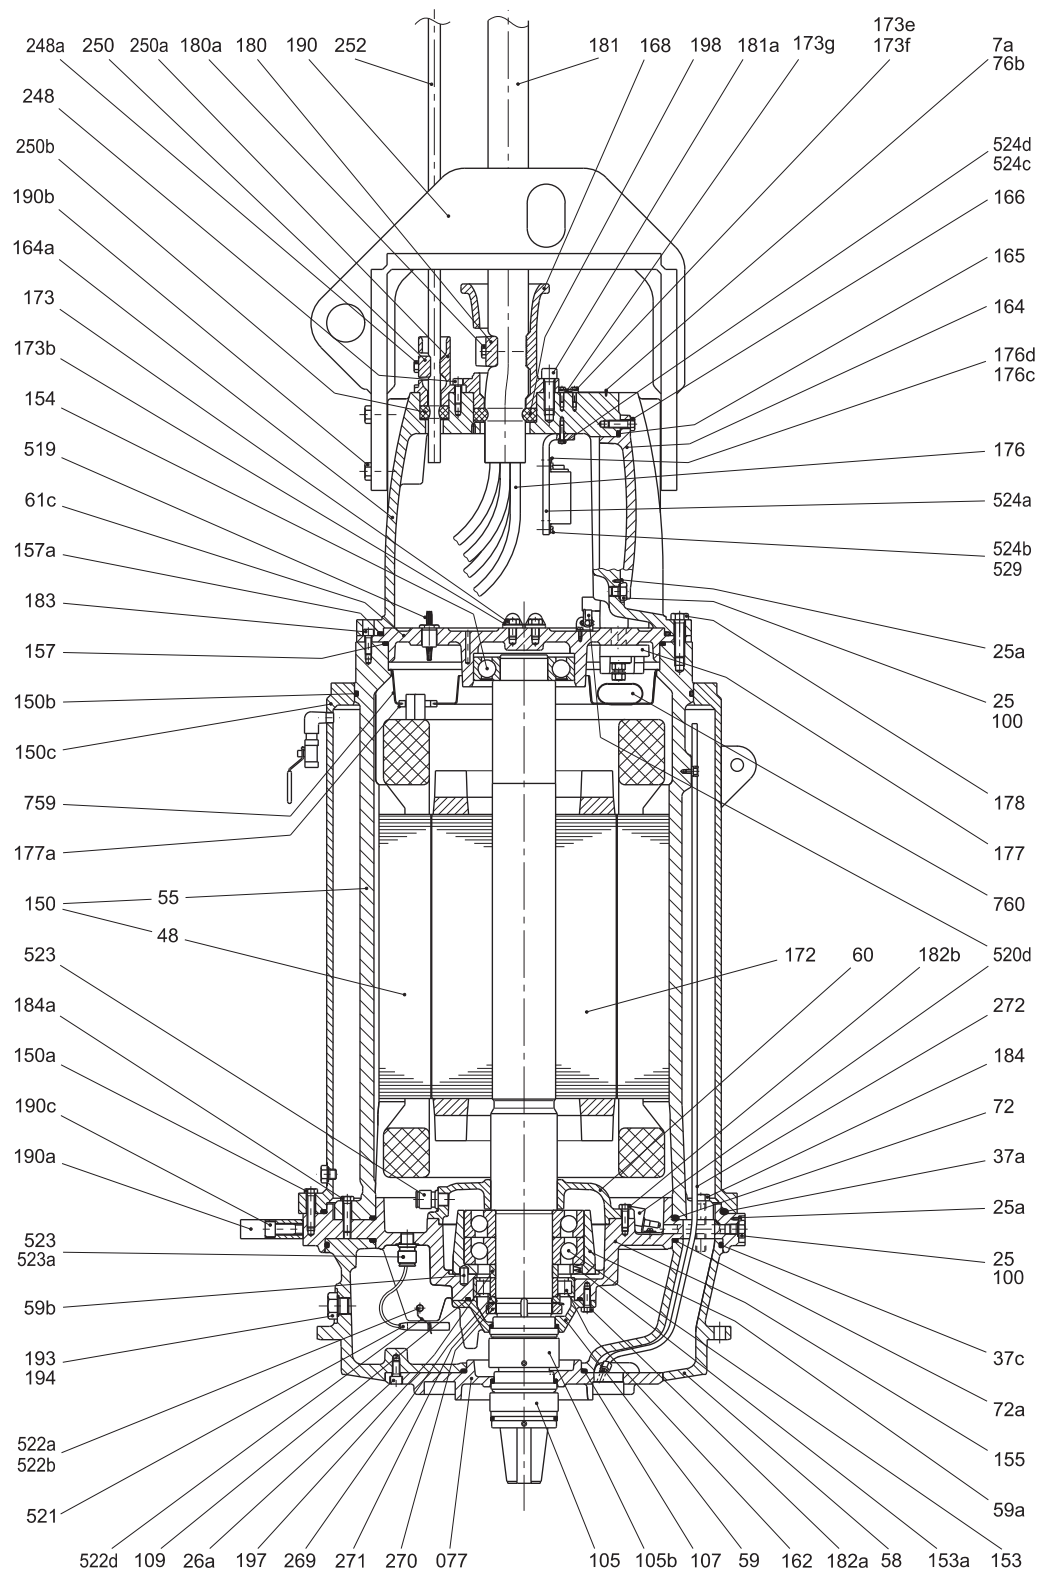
Типоразмер 72, двигатель с охлаждающим кожухом.
